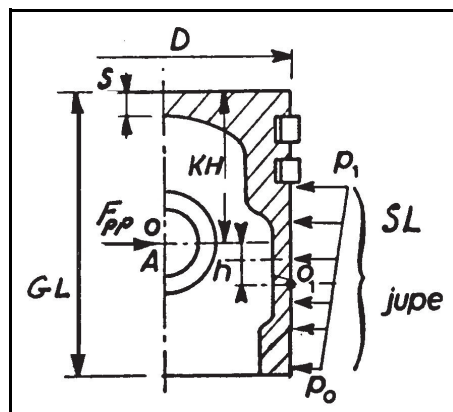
Pression latérale sur la jupe du piston. {Réf. 22}
